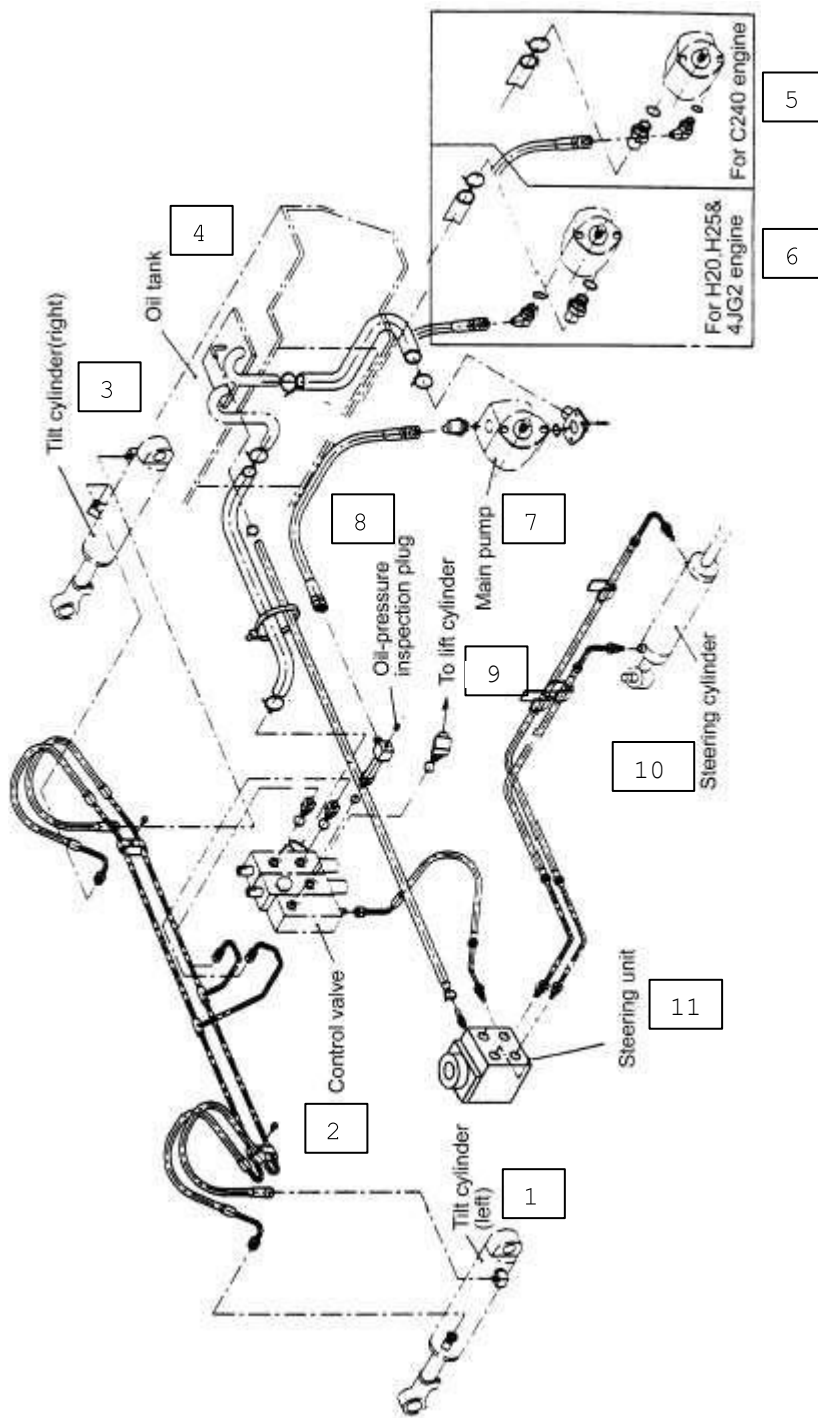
Трубопровод гидравлический (для погрузчиков 2 т и 2,5 т): 1 - цилиндр наклона (левый); 2 - распределительный клапан; 3 - цилиндр наклона (правый); 4 - масляный бак; 5 - для двигателя С240; 6 - для двигателя Н20, Н25 и 4LG2; 7 - главный насос; 8 - патрубок для измерения давления; 9 - к цилиндру подъема; 10 - цилиндр усилителя рулевого управления; 11 - узел усилителя рулевого управления
